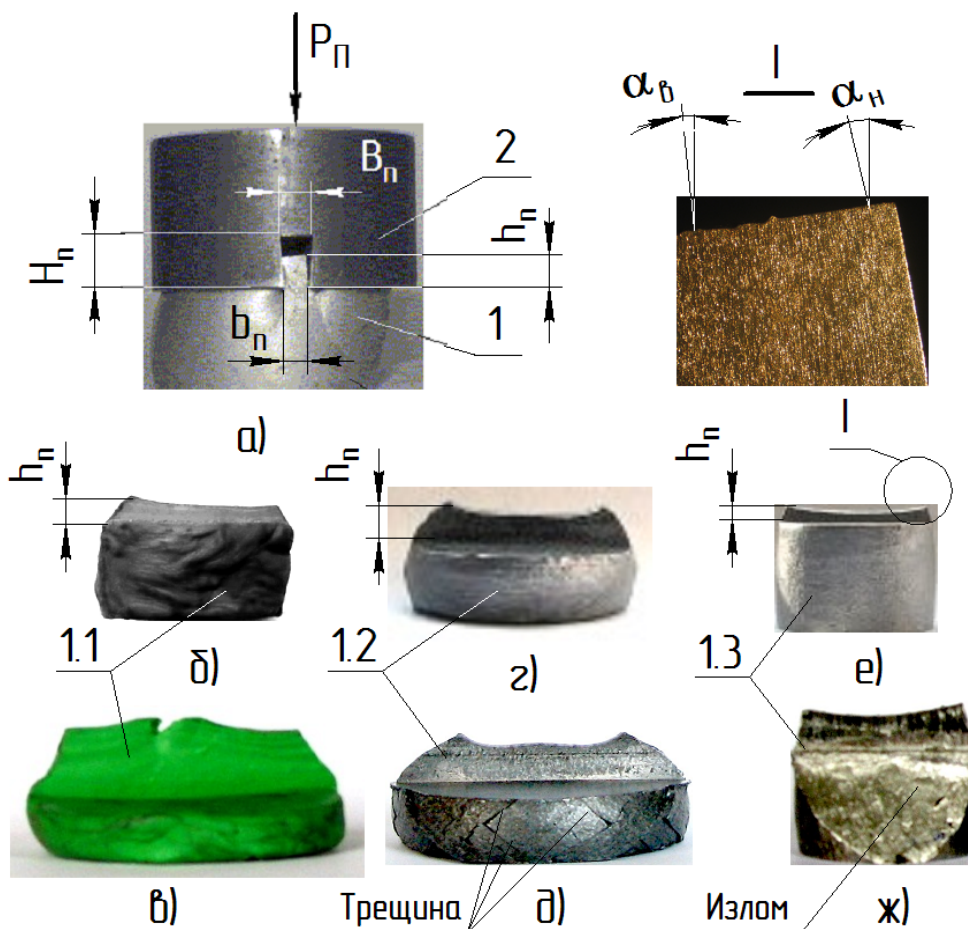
Осадка «без трения» на поверхностях выступа заготовки 1:
